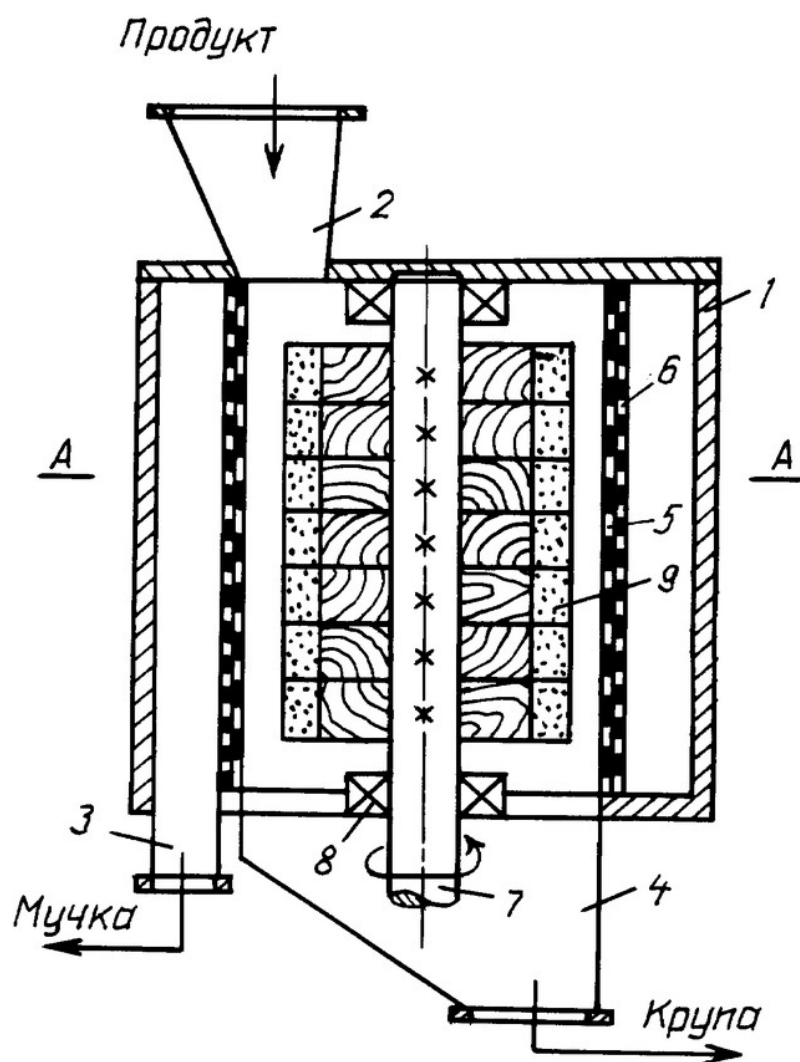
Устройство для шелушения зерна по патенту №2434680
